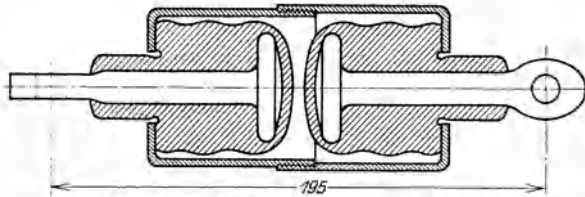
Längsschnitt durch einen Schalldämpfer mit Gummipuffer. Gew. 1,2 kg.
